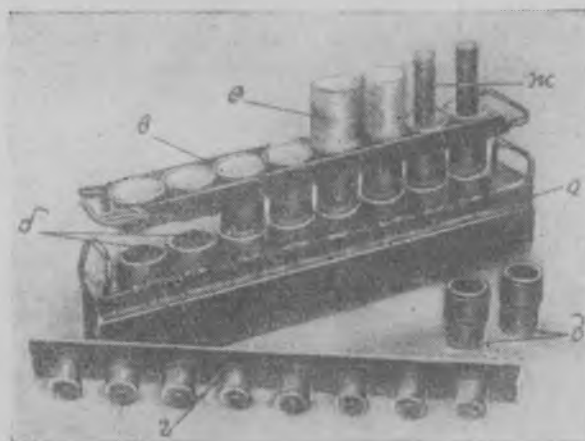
Приспособление для одновременного прессования 8 втулок:
